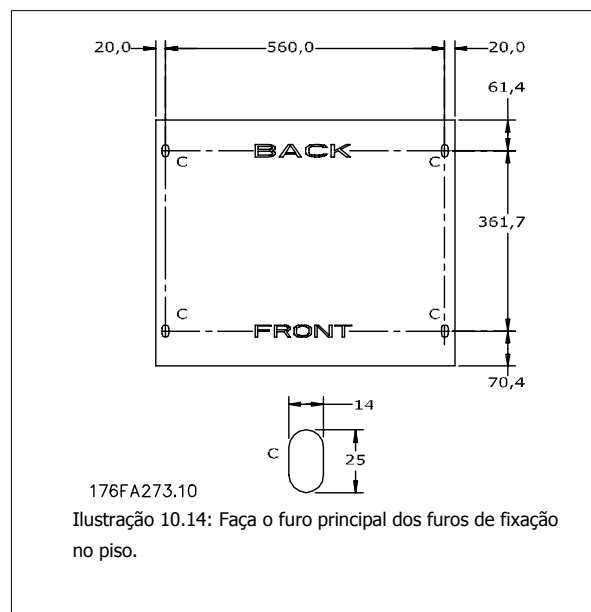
Faça o furo principal dos furos de fixação no piso.
